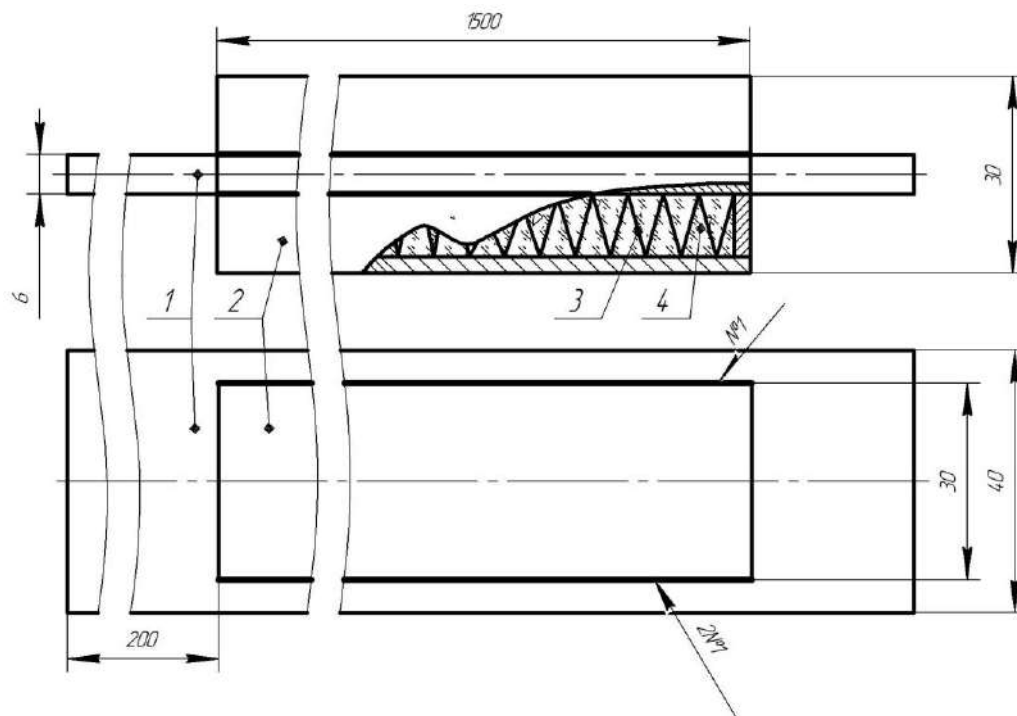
Порошковий електрод, який витрачається, для ЕШН: 1 – сердечник; 2 – коробчаста оболонка; 3 – металева вставка; 4 – шихта
